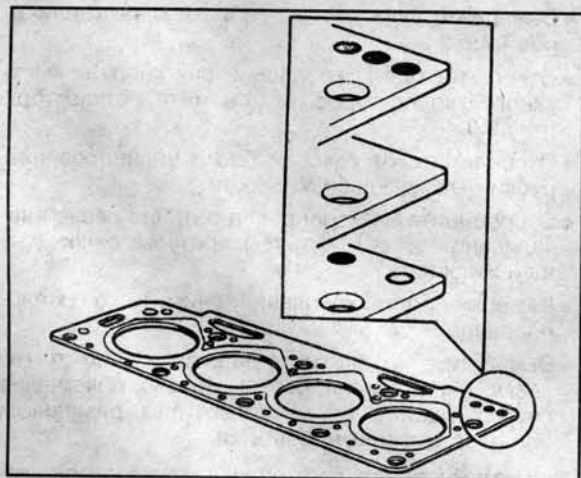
Обозначения на прокладке головки блока цилиндров двигателя D16
